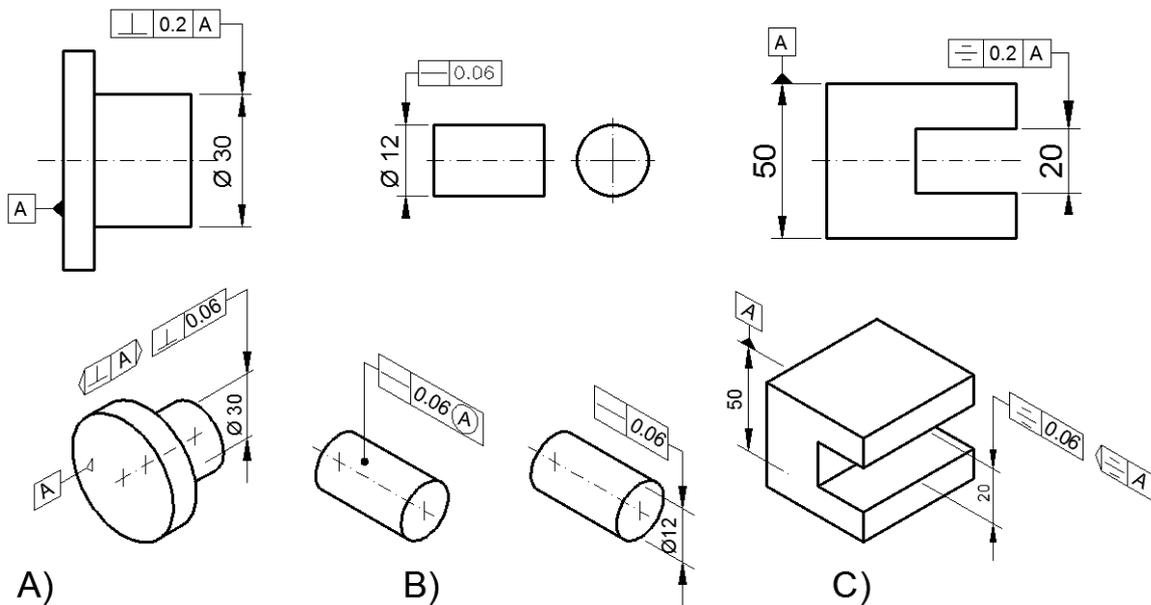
Acotación de tolerancias geométricas. Eje o plano de simetría.
